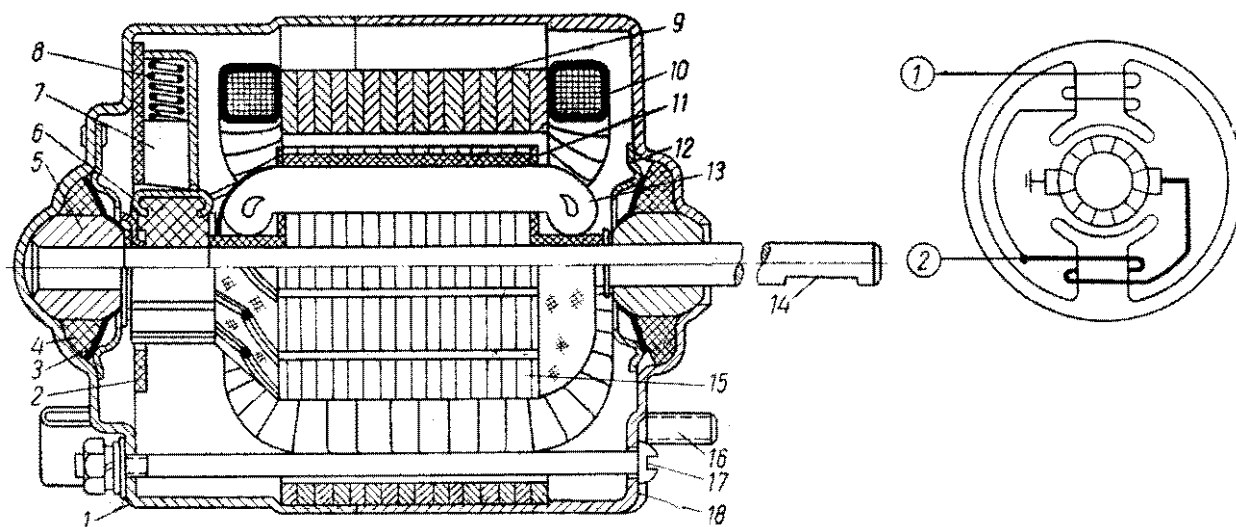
Электродвигатель вентилятора обдува ветрового стекла и обогрева кузова:
